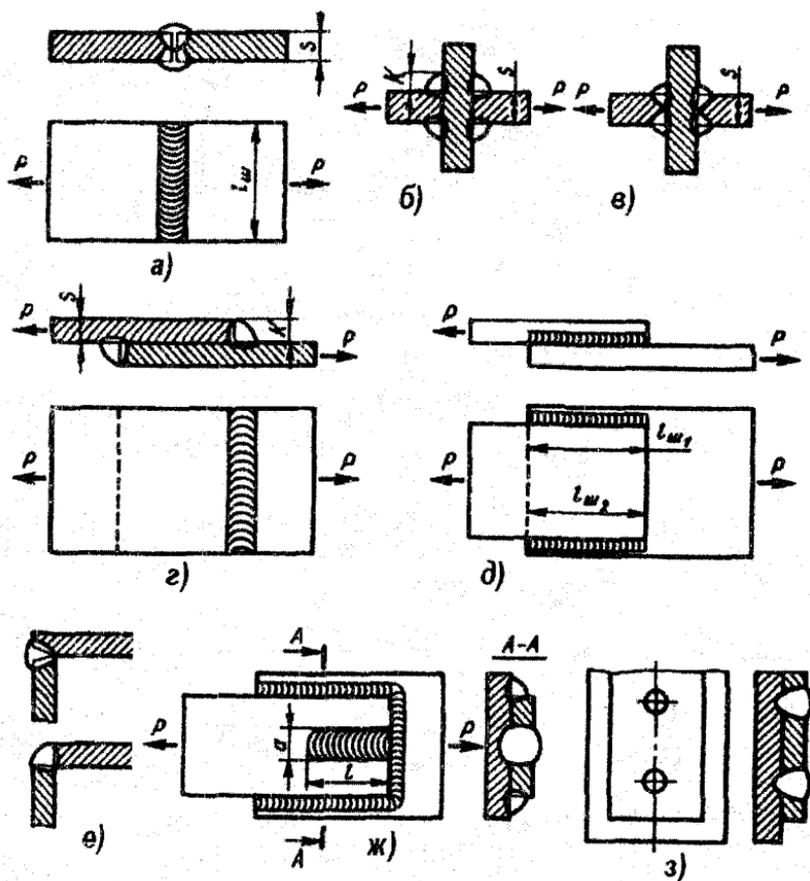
Типи зварних з'єднань: а – встик; б – втавр без підготовки крайків під зварку; в – втавр із підготовкою крайків під зварку; г – внапусток із лобовими швами; д – внапусток із фланговими швами; е – кутове; ж – точкове однозрізне з'єднання внапусток; з – електрозаклепкове; і – прорізне із лобовими і фланговими швами
